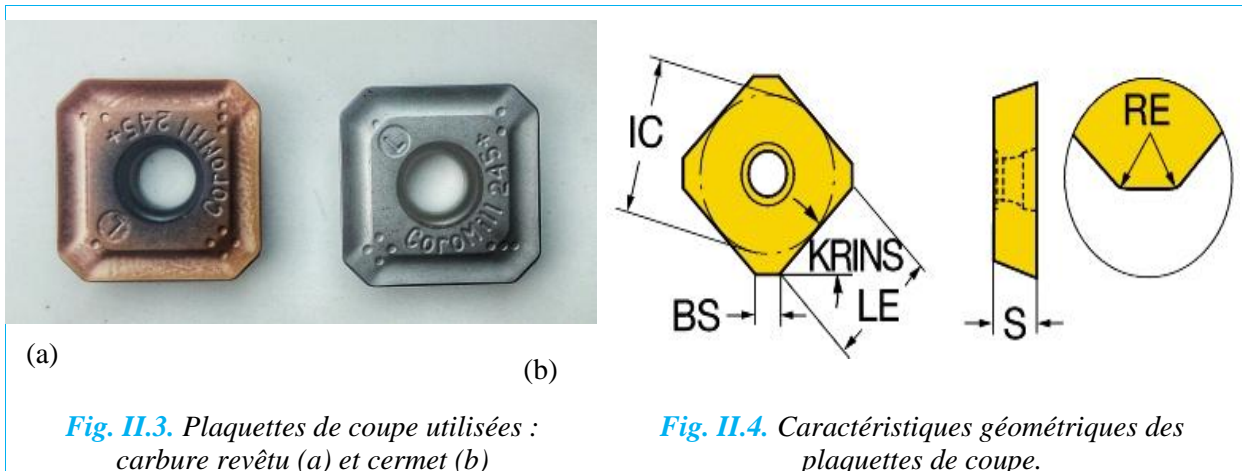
Plaquettes de coupe utilisées : carbure revêtu (a) et cermet (b)
